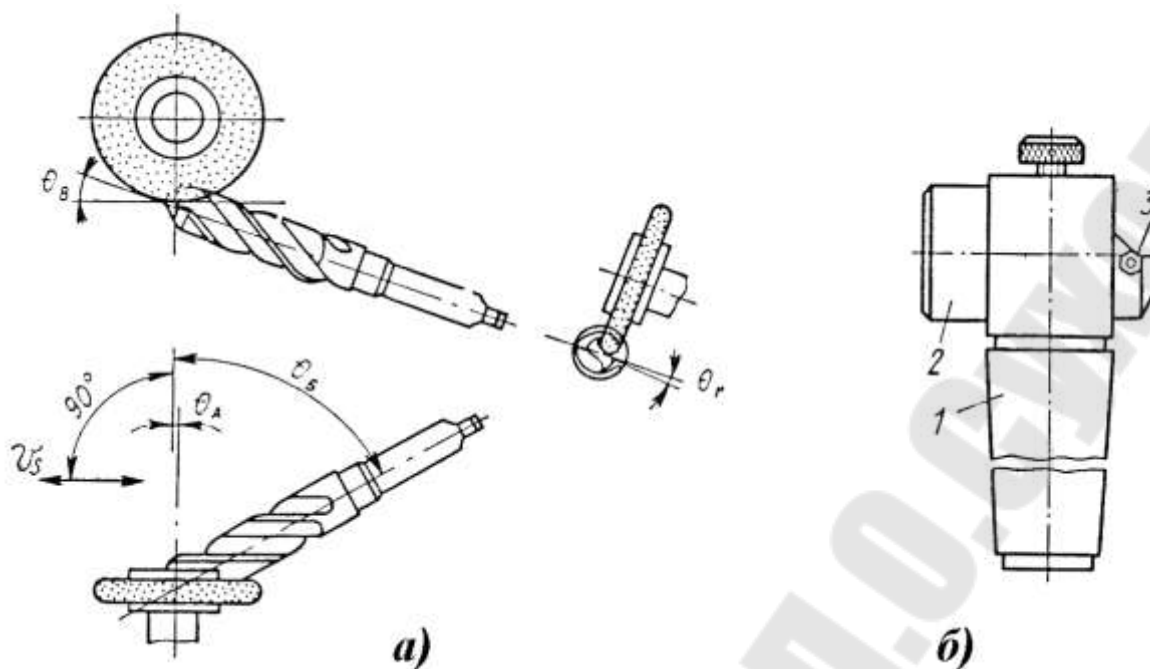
Схема установки абразивного инструмента и сверла при подточке его поперечной кромки (а) и оправка для крепления сверла (б):
